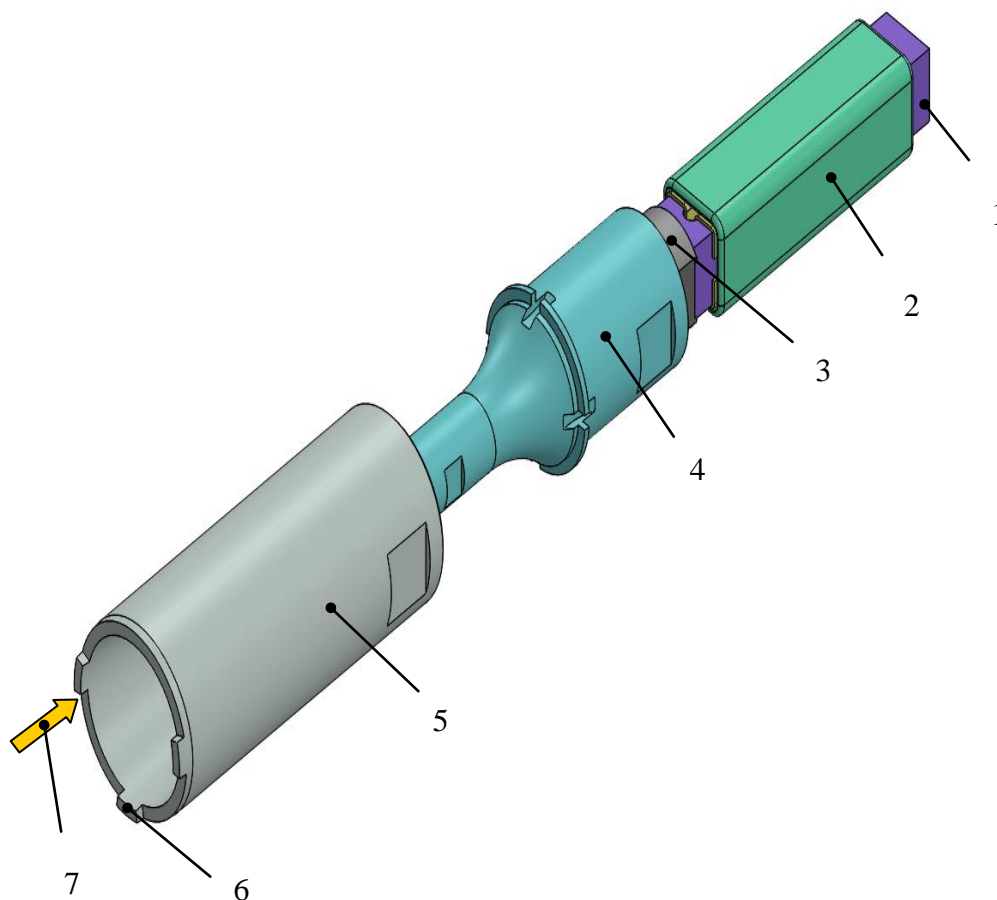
Общий вид УЗКС для трехточечной ультразвуковой сварки: 1 – активный элемент (двигатель); 2 – обмотка подмагничивания-возбуждения; 3 – переходник; 4 – бустер; 5 – волновод; 6 – рабочий торец сварочного волновода; 7 – нагрузка со стороны зоны сварки
